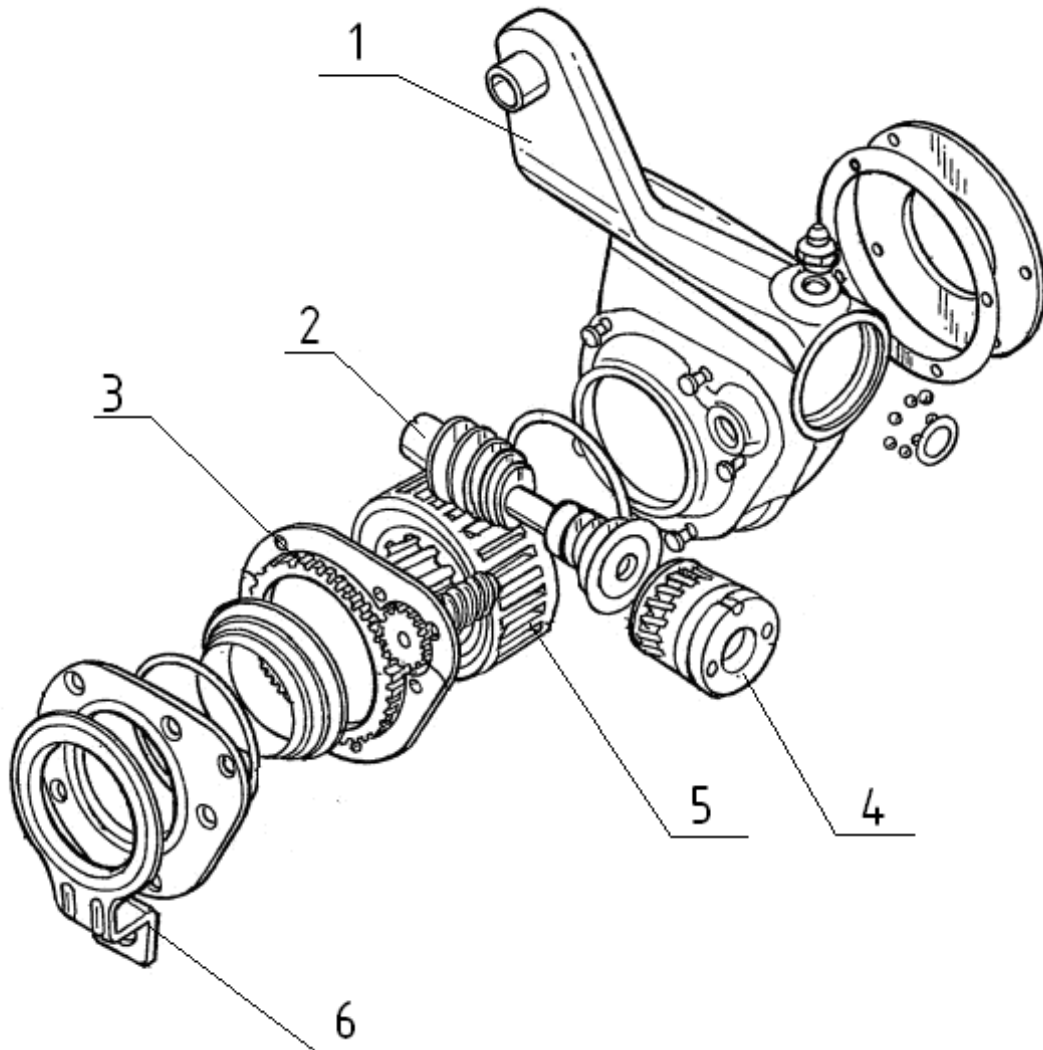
Автоматический регулятор зазора тормозных колодок, встроенный в тормозной рычаг: 1 – рычаг; 2 – червячный вал; 3 – зубчатая передача; 4 – регулировочное устройство; 5 – червячное колесо; 6 – опорное плечо
